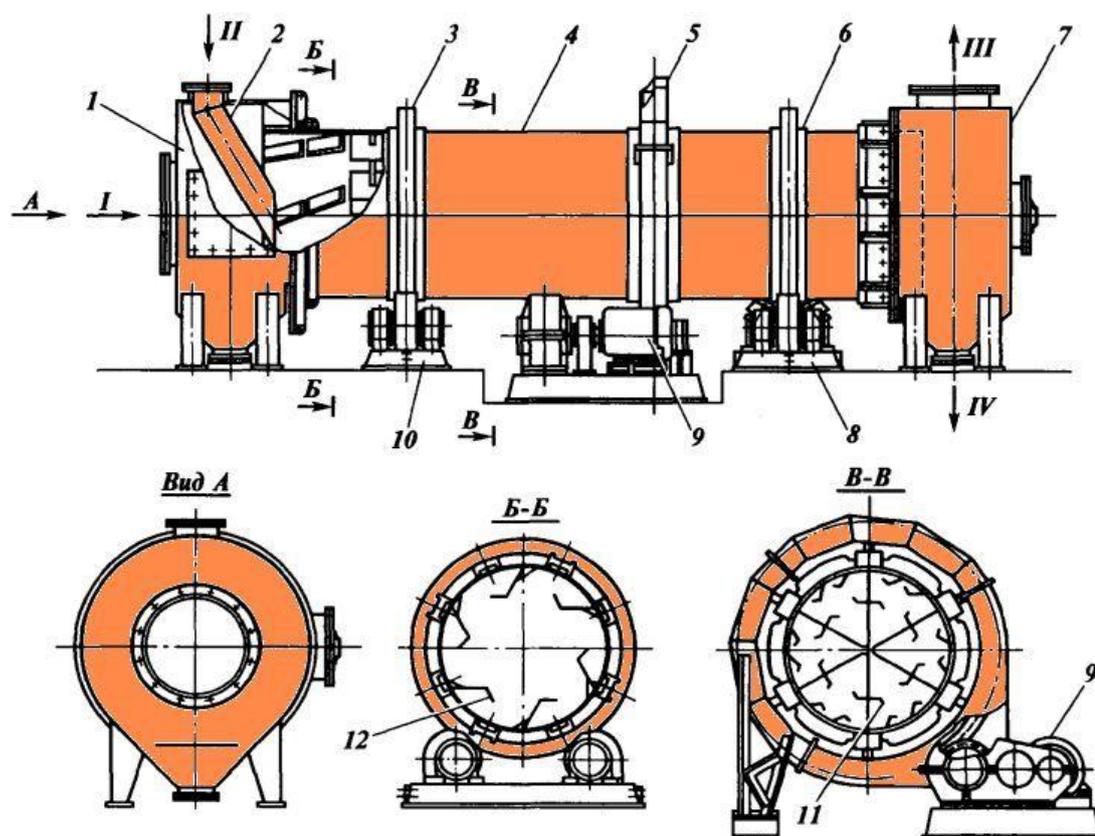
Барабанная сушилка. 1 - загрузочная камера; 2 - наклонный лоток; 3 - бандаж; 4 - барабан; 5 - зубчатый венец; 6 - кольцевые накладки; 7 - разгрузочная камера; 8 - упорные ролики; 9 - привод; 10 - опорные ролики; 11 - секторная перевалочная насадка; 12 - лопастная насадка.
